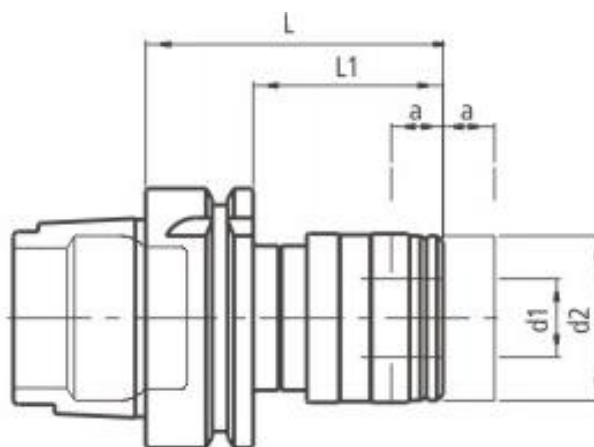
Резьбонарезной патрон D'ANDREA TOPRUN
